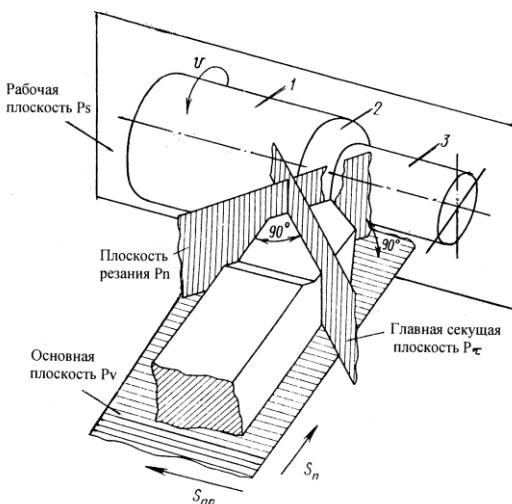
Поверхности заготовки и координатные плоскости резца:
